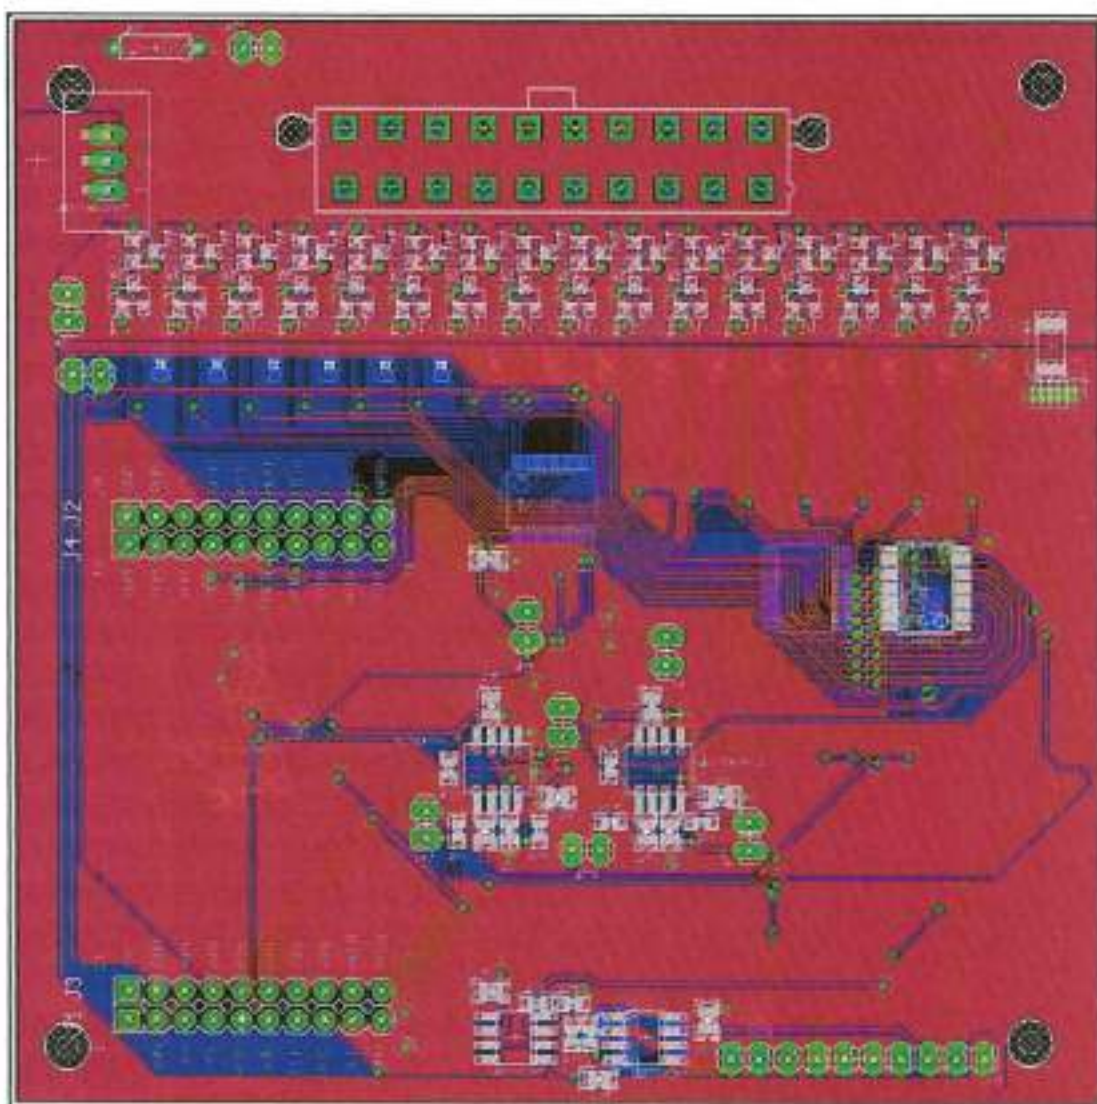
Layout PCB. [Fonte: Autor, 2015]
